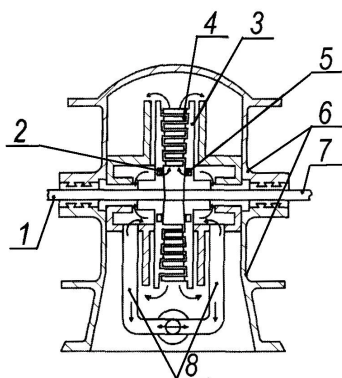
Конструктивная схема турбины Юнгстрема [9]: 1, 7 – валы; 2, 5 – диски турбины; 3, 4 – рабочие лопатки; 6 – корпус; 8 – паропровод
